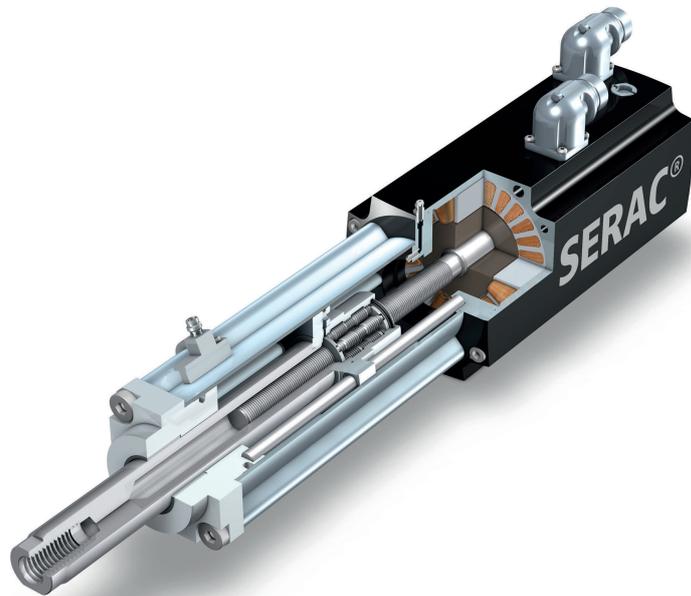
Elektrozyylinder „Serac LH“ – modularer Aufbau für unterschiedlichste Lösungen: Die Spindel-mutter wird direkt durch einen Hohlwellen-Torque-Motor angetrieben. (Bild: Ortlieb)
